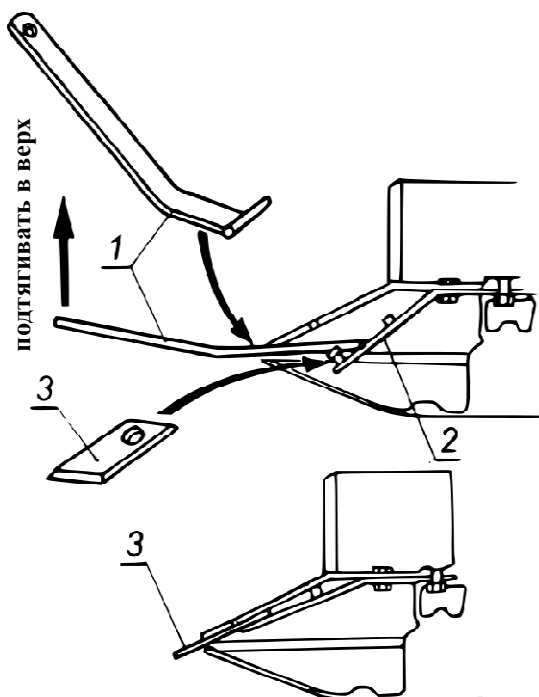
Способ установки ножей на рабочих тарелках: 1 – специальный ключ; 2 – держатель ножа; 3 – нож
